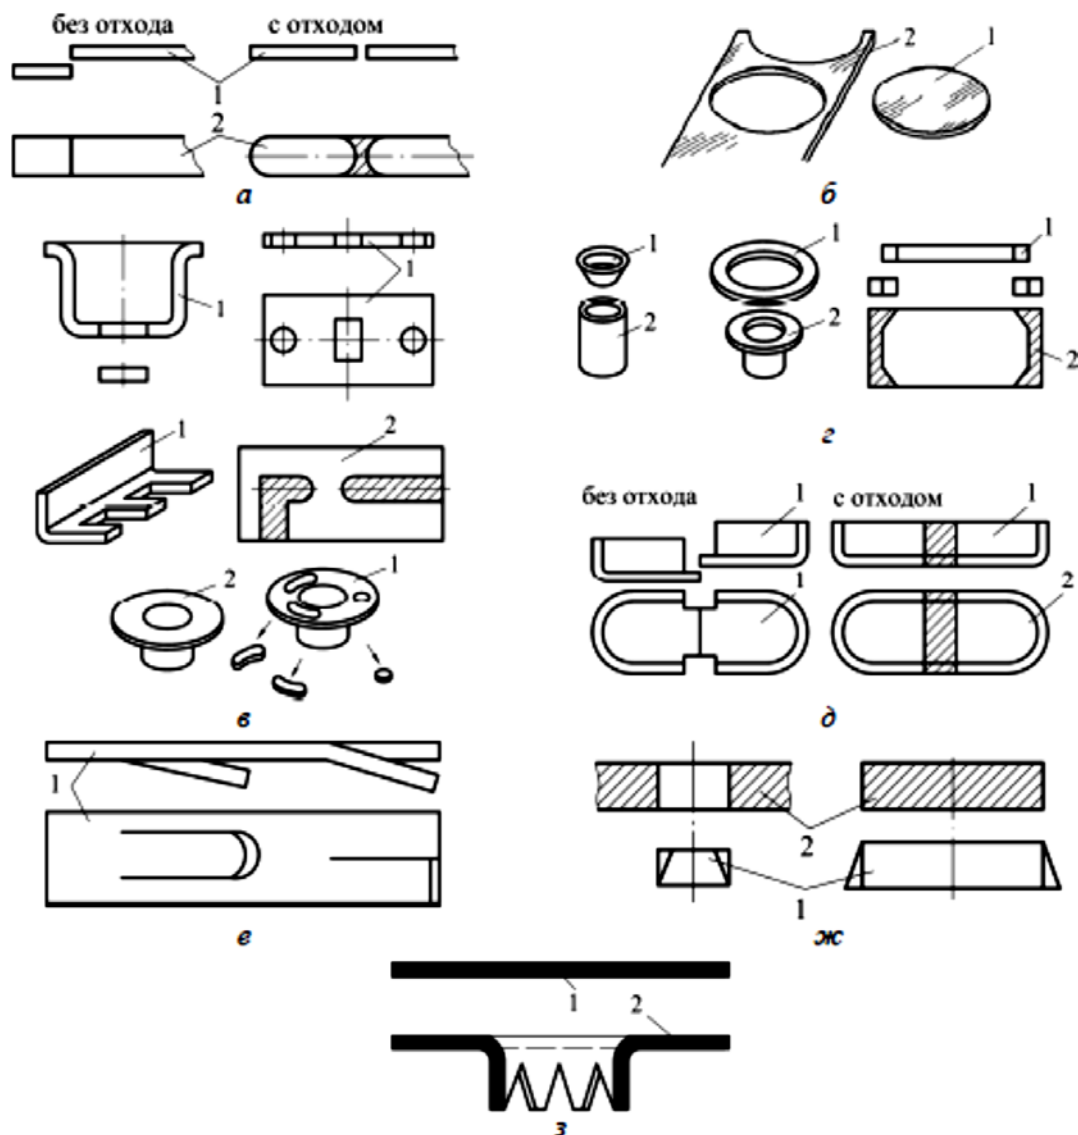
Деталь (1) и исходная заготовка (2), полученная разделительной операцией листовой штамповки: а – отрезкой; б – вырубкой; в – пробивкой; г – обрезкой; д – разрезкой; е – надрезкой; ж – зачисткой; з – проколкой
